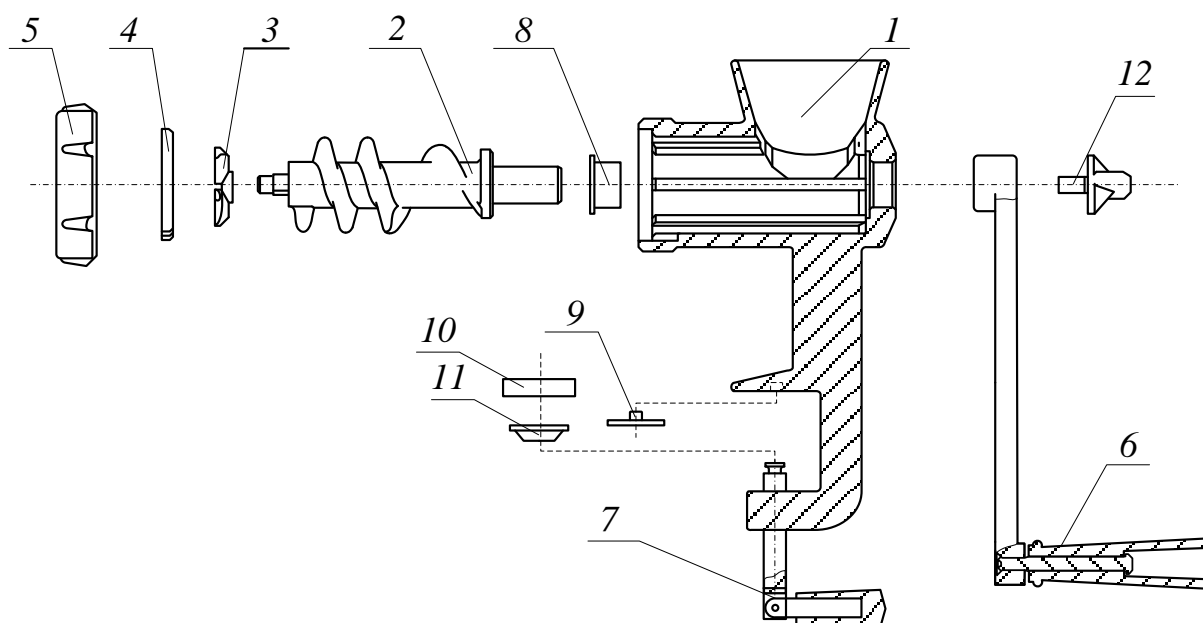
Схема сборки первоначального варианта механизма мясорубки: 1 – корпус; 2 – шнековый вал; 3 – нож; 4 – решетка; 5 – накидная гайка; 6 – рукоятка (подборка); 7 – винт струбины (подборка); 8 – втулка; 9 – подкладка (2 шт.); 10 – подкладка для клапана; 11 – клапан; 12 – винт прижимной (подборка)
